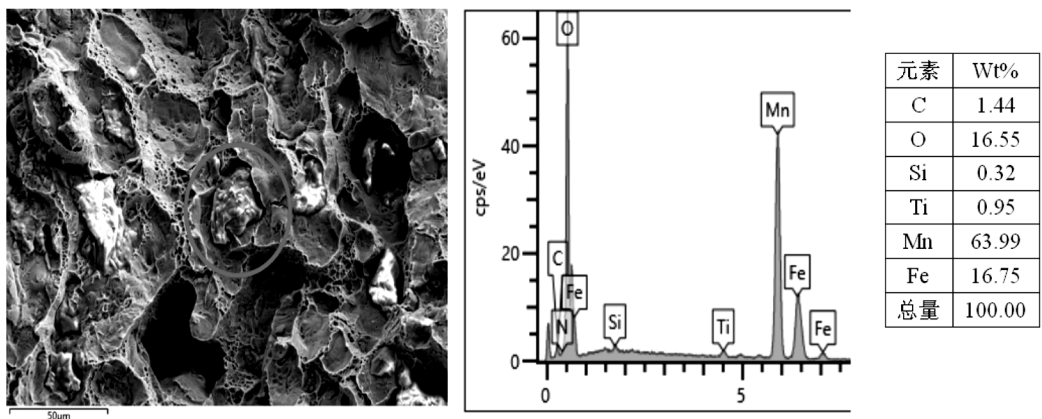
焊缝冲击断口形貌及夹杂物能谱分析
